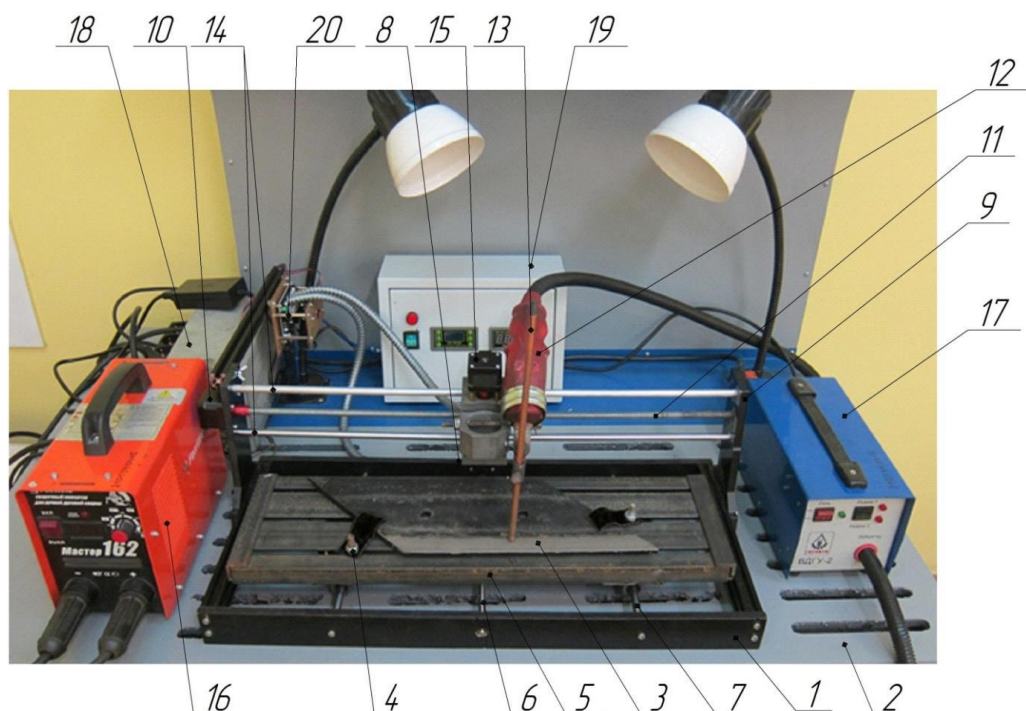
Установка для формування металокерамічних покриттів методом КВДЗ: 1 – основа; 2 – зварювальний стіл ССН-01-03; 3 – робочий орган, на ріжучо-лезовій частині якого формується металокерамічне покриття; 4 – притискач; 5 – рухомий стіл; 6 – гвинт поперечного переміщення стола; 7, 14 – напрямні; 8, 10, 15 – крокові електродвигуни; 9 – кронштейни; 11 – гвинт поздовжнього переміщення; 12 – вібратор; 13 – вугільний електрод; 16 – зварювальний інвертор; 17 – пристрій для зміни частоти коливань вугільного електрода під час КВДЗ; 18 – блок живлення; 19 – блок керування; 20 – керувальний модуль із знятим захисним кожухом [3].
